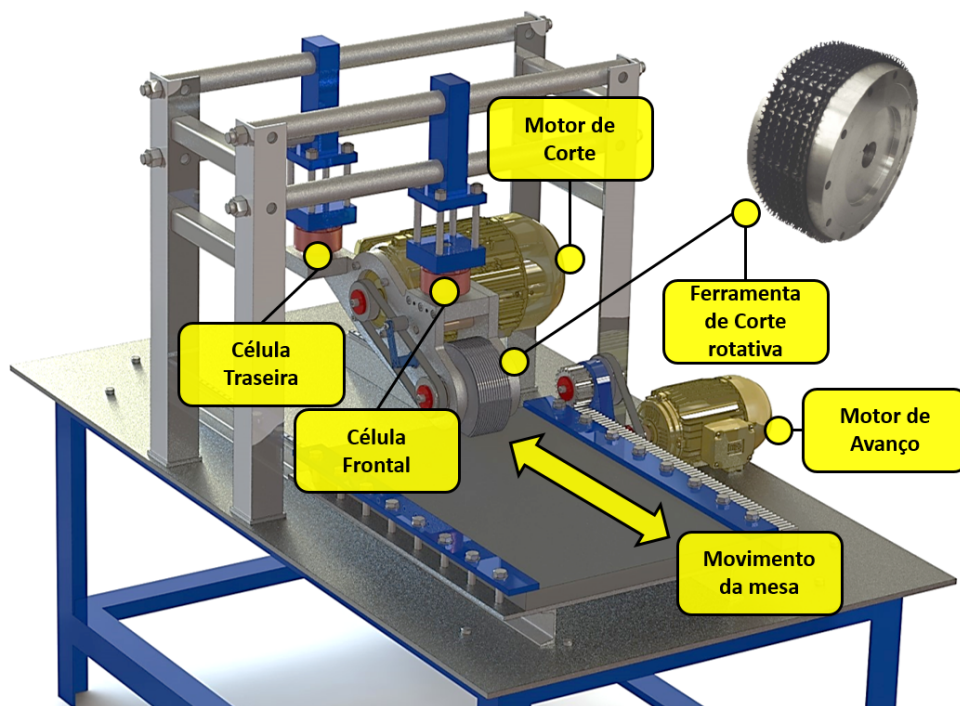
Principais componentes da bancada de ensaios projetada.
